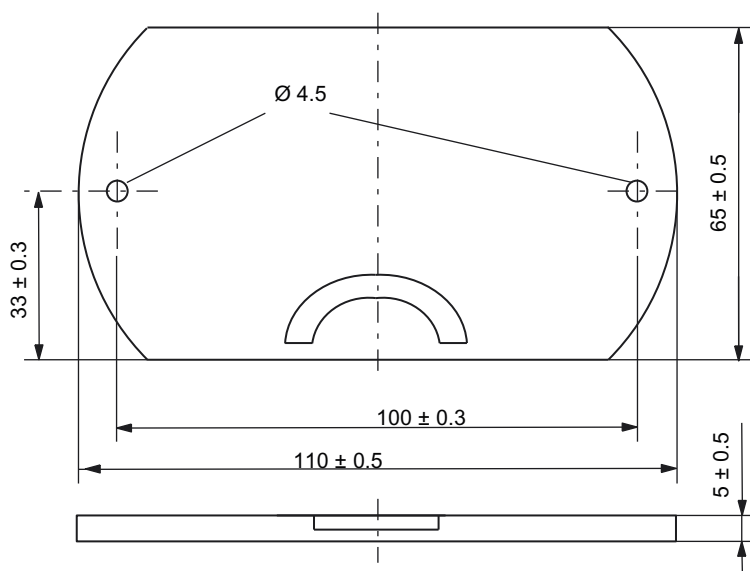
固定座 6GT2390-0AA00 的尺寸图
